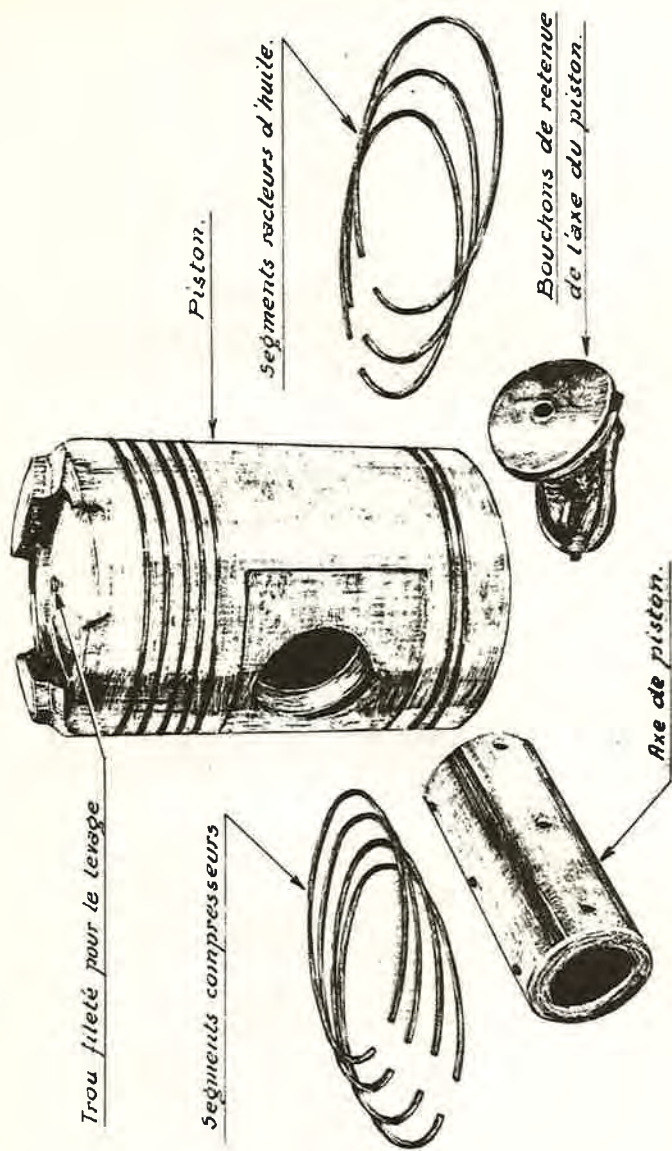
PISTON ET SEGMENTS DU MOTEUR BALDWIN.
